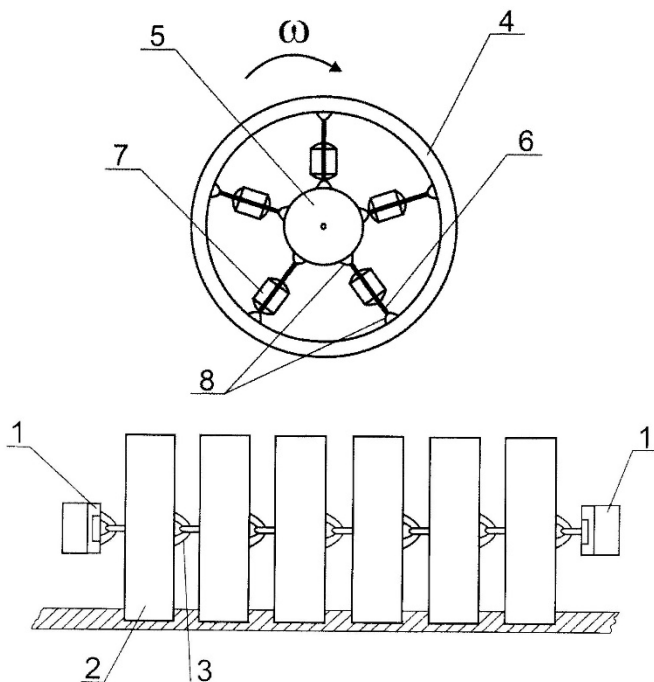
, 3 - Каток вибрационного действия: 1 - подшипниковые узлы; 2 - рабочие органы; 3 - крестообразные шарниры; 4 - кольцевая часть; 5 - диск; 6 - спицы; 7 - цилиндрические ударники; 8 - полушаровые наковальни.
